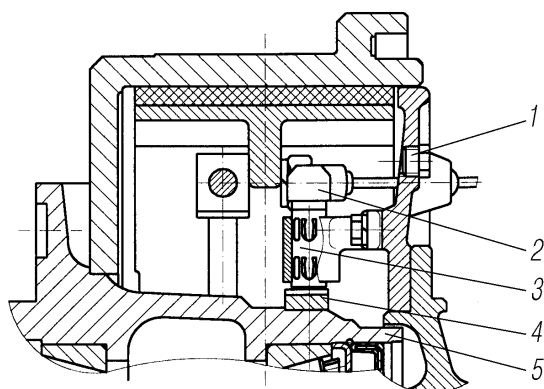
Механизм тормозной колесный: 1- пробка; 2- датчик индуктивный; 3- втулка зажимная; 4- кольцо импульсное зубчатое; 5- ступица колеса
